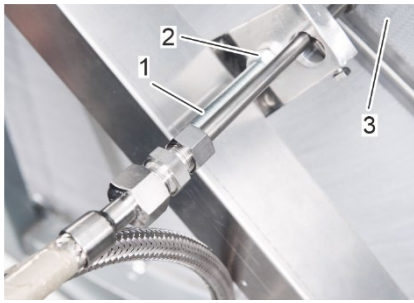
Ajuste de la distancia entre la boquilla de aire comprimido y la superficie del rotor
